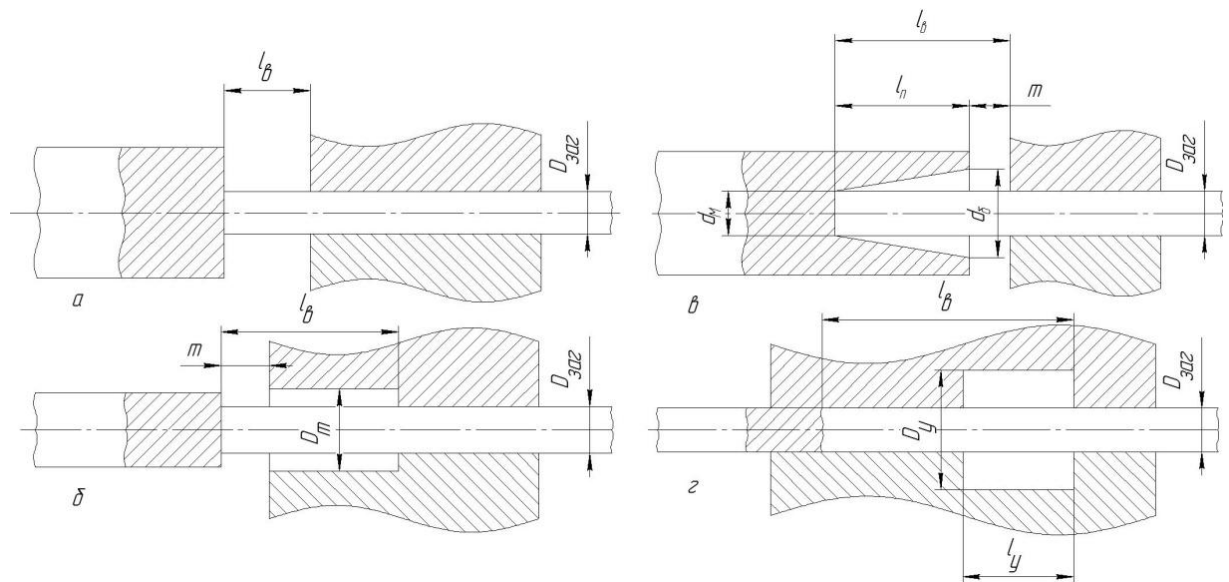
Форма ручьев для набора металла и расположение заготовки в ручье: а – конец заготовки не зажат; б – в цилиндрической матрице; в – в коническом пуансоне; г – конец заготовки не выступает за пределы матрицы
